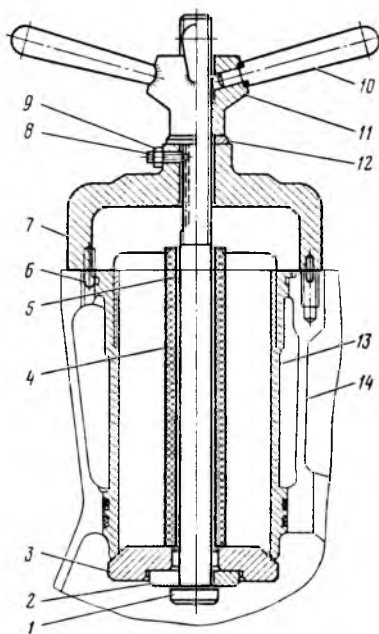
Приспособление для выпрессовки гильзы из блока цилиндров двигателя:
